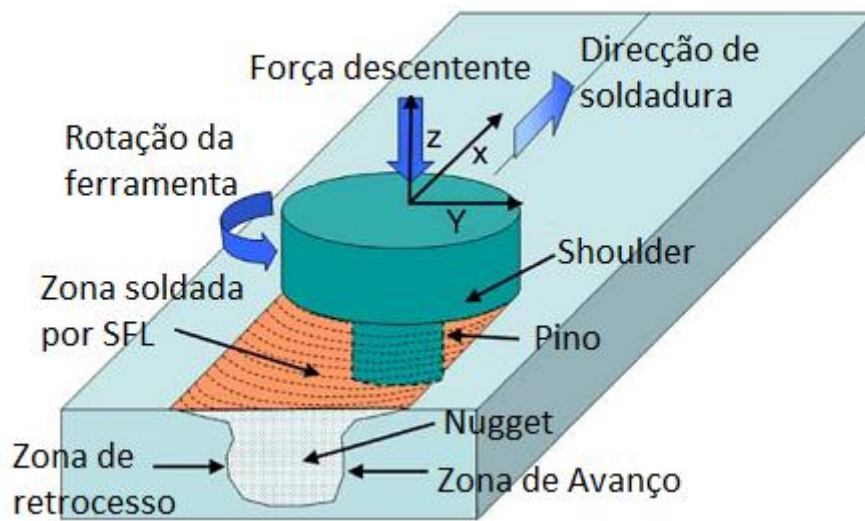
Funcionamento da soldadura por fricção linear (adaptada) [1]
